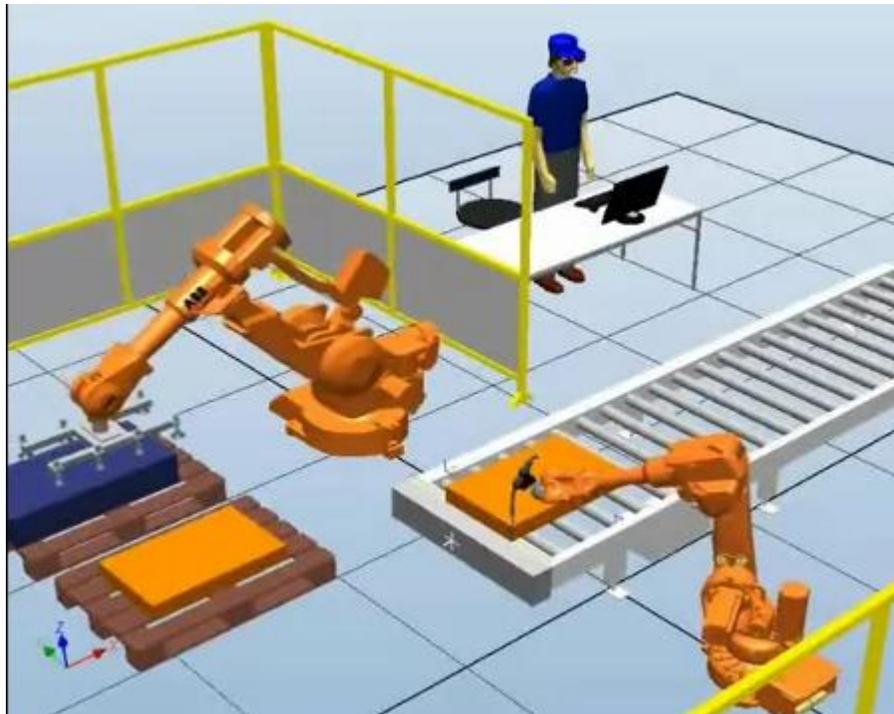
Soldadura al vuelo en banda transportadora [Robotestudio (2012)]
